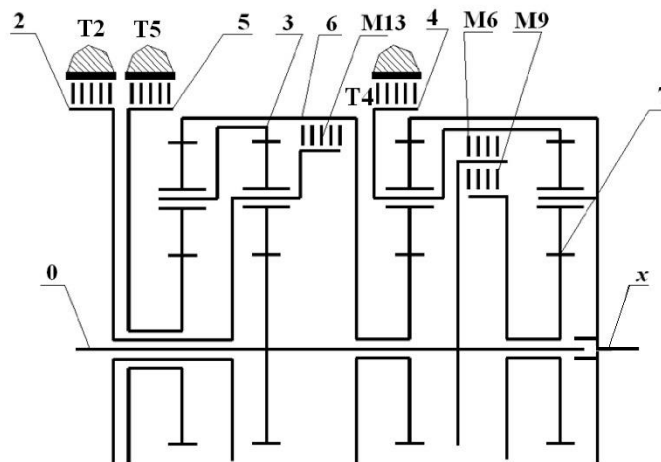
Кінематична схема планетарної коробки передач
